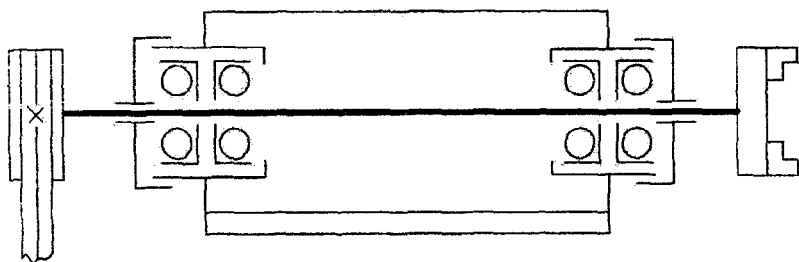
Кинематическая схема автономной шпиндельной бабки токарного станка
